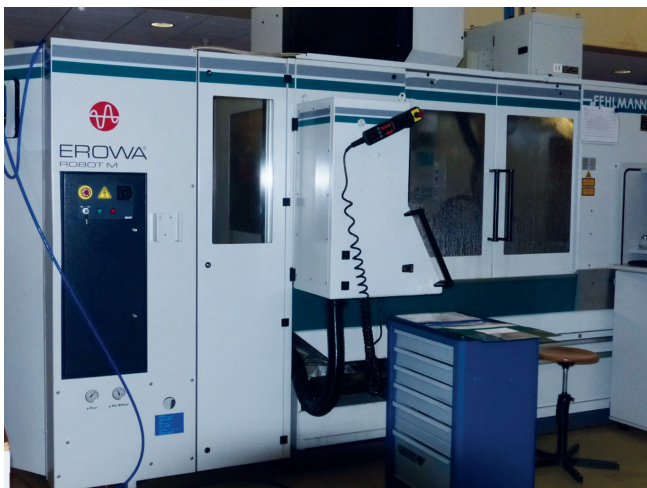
Auf diesen Maschinen wird seit dem Jahr 2000 das gleiche Werkstückspektrum mit Toleranzen innerhalb weniger Hundertstel Millimeter gefertigt
